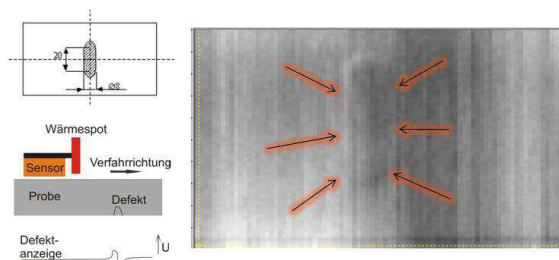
UDIMET-720[®]-Platte mit Waspaloy[®]-Auftragsschweißung auf der Unterseite. Links: technische Zeichnung des Defektes und schematische Darstellung der Prüfsituation. Rechts: gemessenes Magnetfeld in Schwarz-Weiß-Darstellung.
